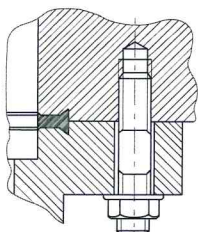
Flanschverbindung CF-F, Stiftschraube und Gewindebohrung
